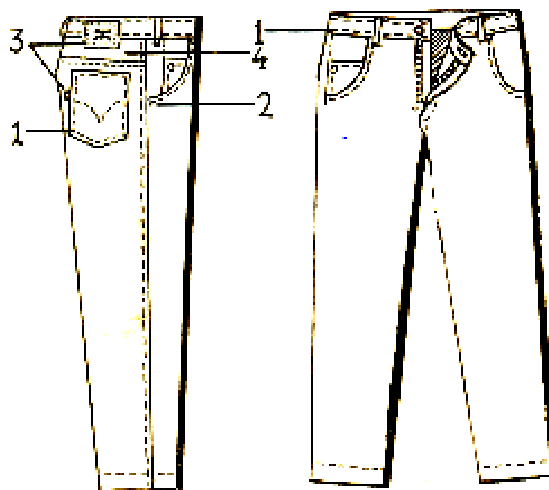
Джинсы: 1 – декоративная строчка; 2 – заклепка; 3 – знаки фирмы-изготовителя; 4 – кокетка
